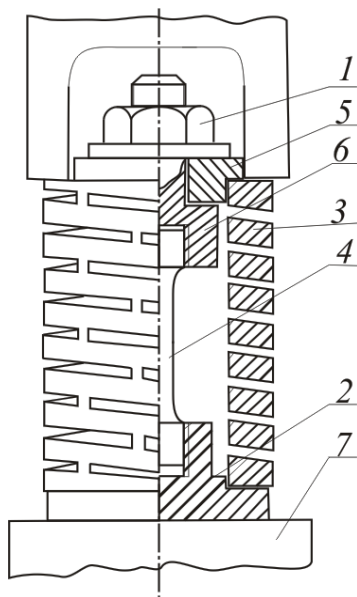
Схема приспособления для нагружения образца при испытании на замедленное разрушение:
